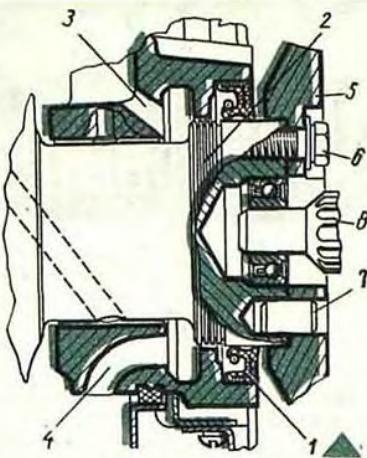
Уплотнение заднего конца коленчатого вала: 1 — самоподжимной сальник с резьбой; 2 — маслосгонная резьба; 3 — дополнительное отверстие; 4 — сливной канал; 5 — маховик; 6 — болт крепления маховика; 7 — установочный штифт; 8 — передний конец ведущего вала коробки передач.
